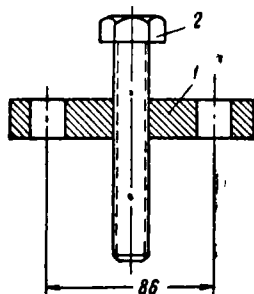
Приспособление для выпрессовки пальцев кронштейнов щеткодержателей:
